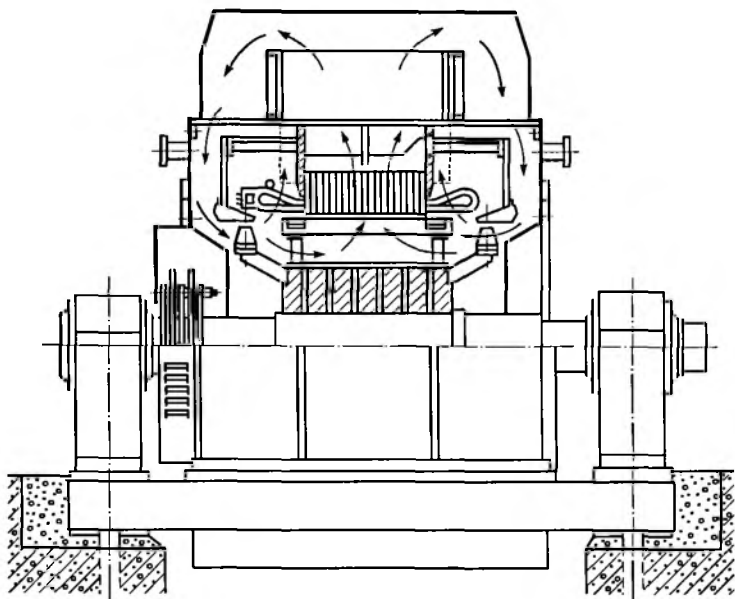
Трехфазный синхронный двигатель со стоячковыми подшипниками исполнения по степени защиты IP44 и способу охлаждения ICW37A81
